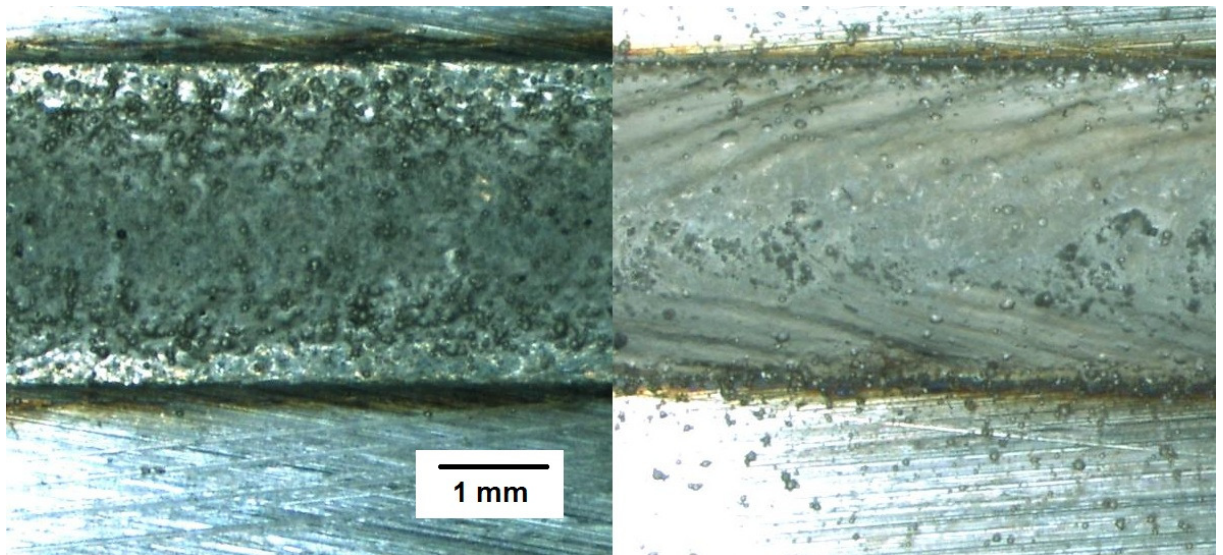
Auftragschweißspur ohne (links) und mit (rechts) Gasdruckminimierung
